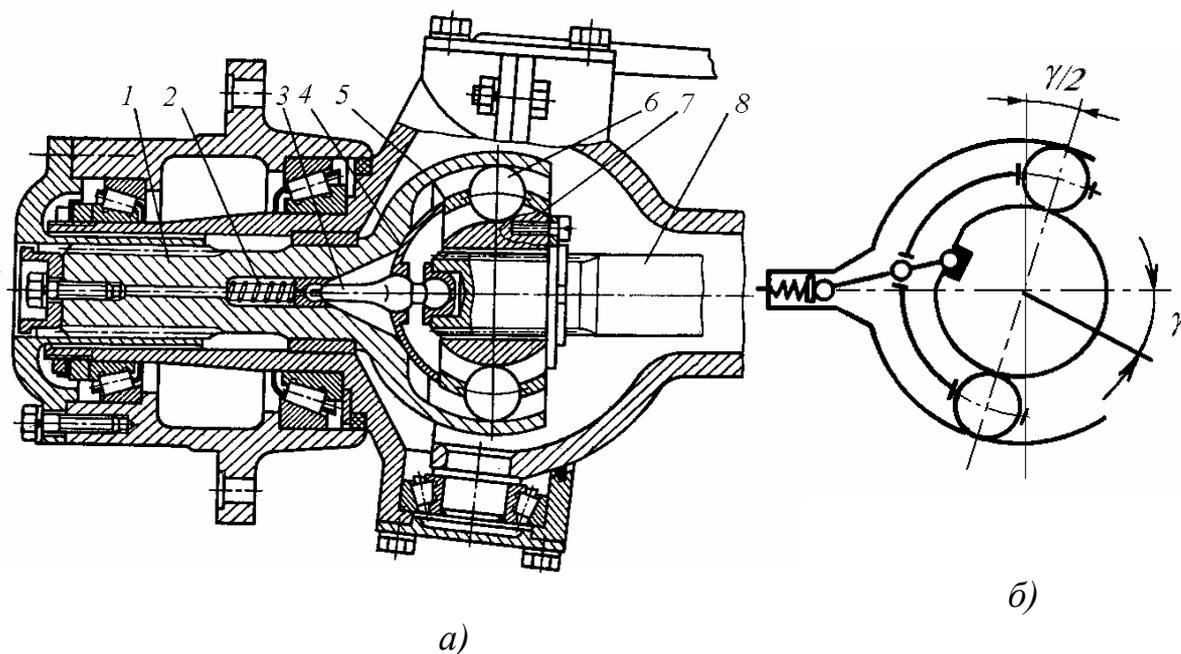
Шестишариковый карданный шарнир с делительным рычажком типа “Рсцепп”:
